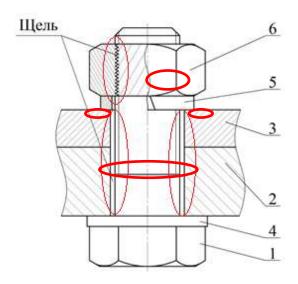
Щели в резьбовом соединении и стыках соединяемых элементов: 1 — болт; 2,3 — соединяемые детали; 4 — шайба плоская; 5 — шайба пружинная; 6 — гайка
